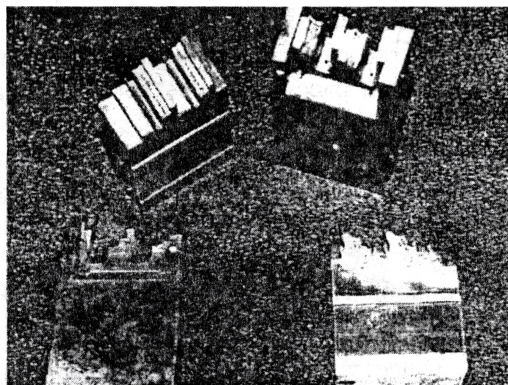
Фильеры для литья уплотнителя холодильника, восстановленные лазерной наплавкой
